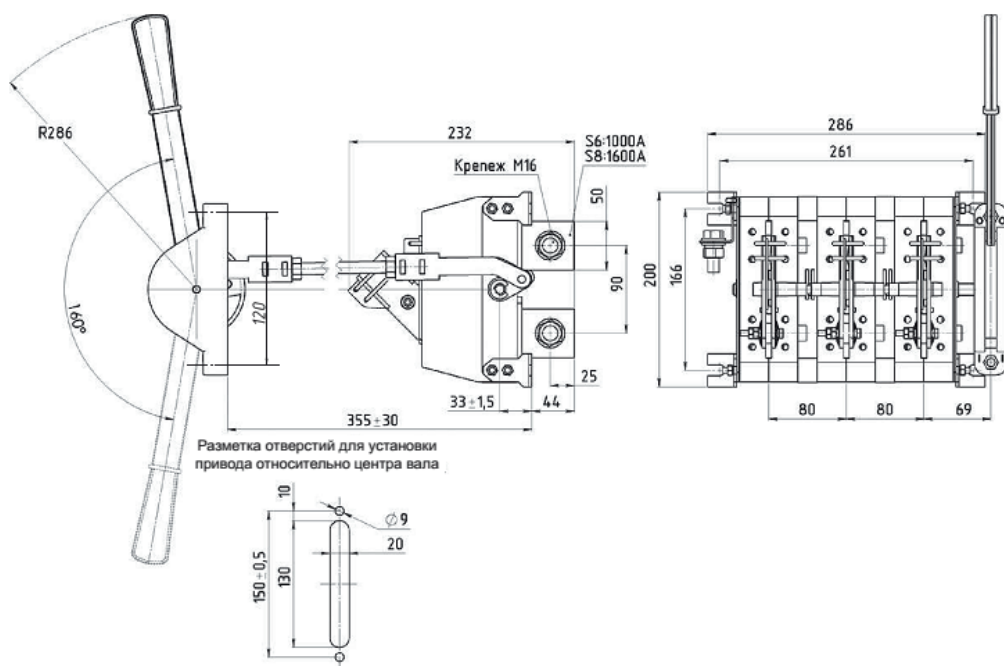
Разъединитель РЕ19-41(43)-31150-00 УХЛЗ с боковой смещенной рукояткой
